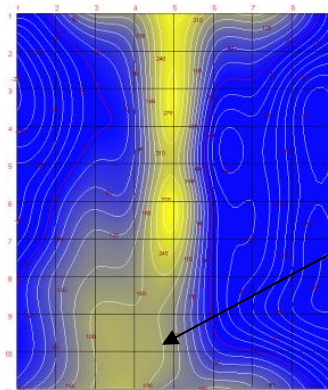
Металлические пластины с непроваренным сварным швом.
